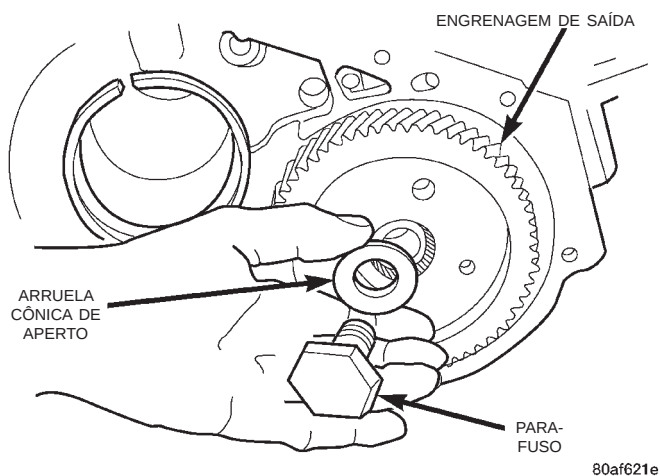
Parafuso e Arruela da Engrenagem de Saída
